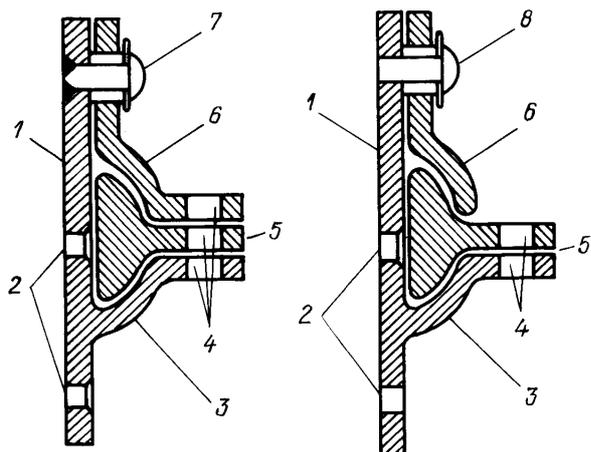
Приспособления для наложения таможенных печатей и пломб:
